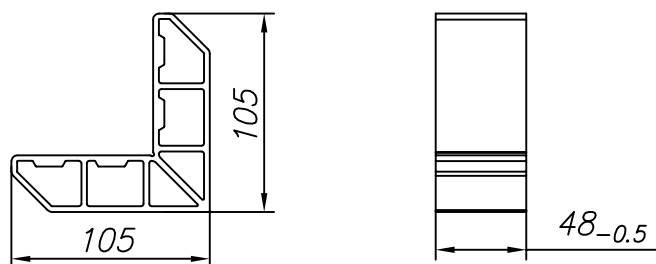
Изготовление соединителя углового FLGU.400.0910
